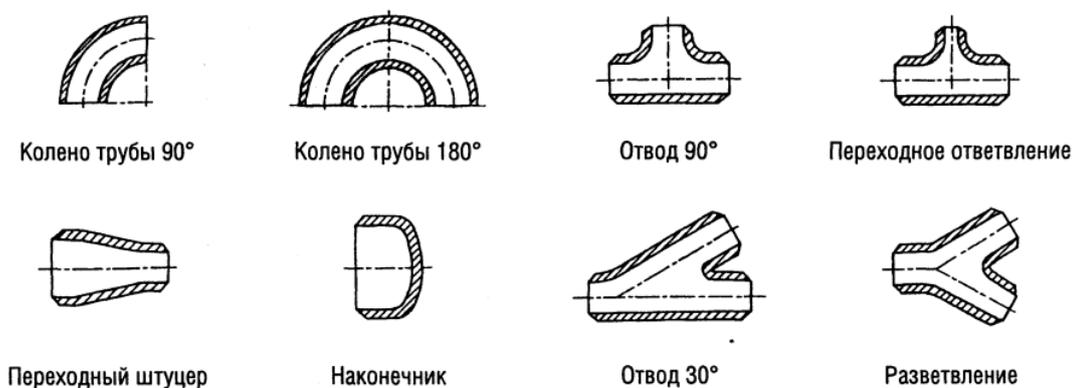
Фасонные части труб для сварки
